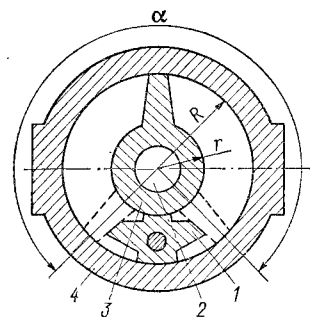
Поворотный гидро-двигатель: 1 — разделитель; 2 — вал; 3 — шибер; 4 — корпус
